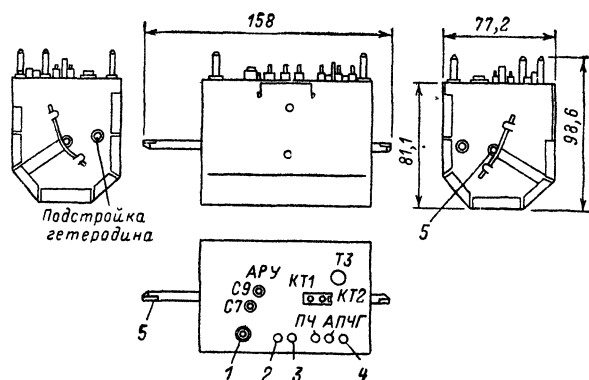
Габаритный чертеж селектора каналов СК-М-15.
